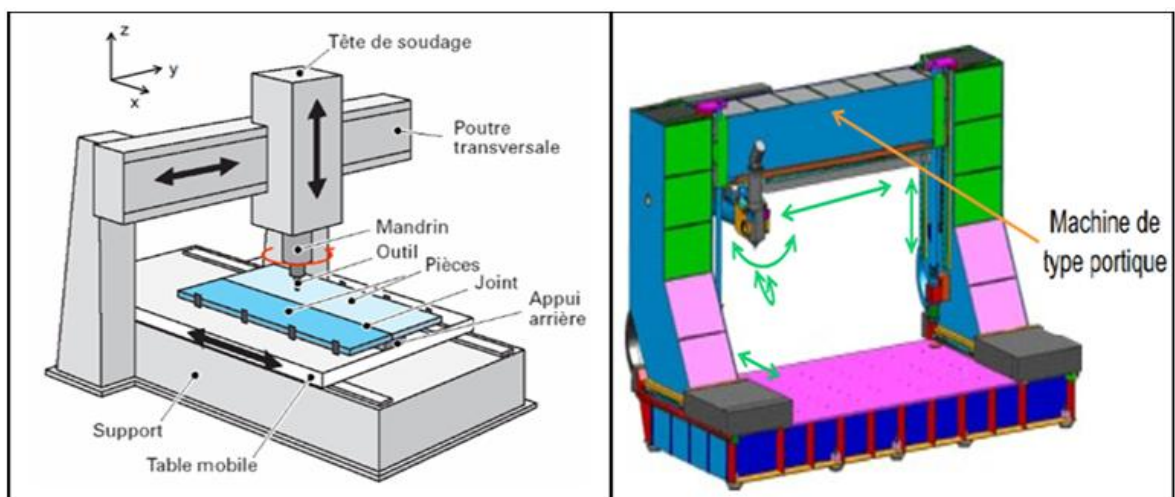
Schéma des machines-outils pour le FSW [34].
